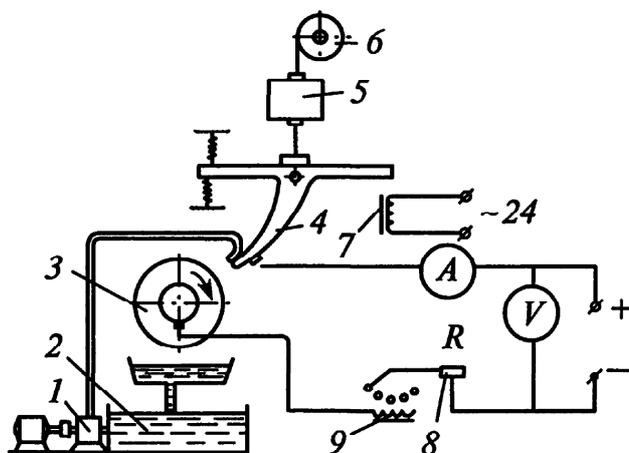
Схема установки для вибродуговой наплавки: 1 – насос; 2 – бак; 3 – деталь; 4 – мундштук; 5 – механизм подачи; 6 – кассета; 7 – вибратор; 8 – реостат; 9 – дроссель
